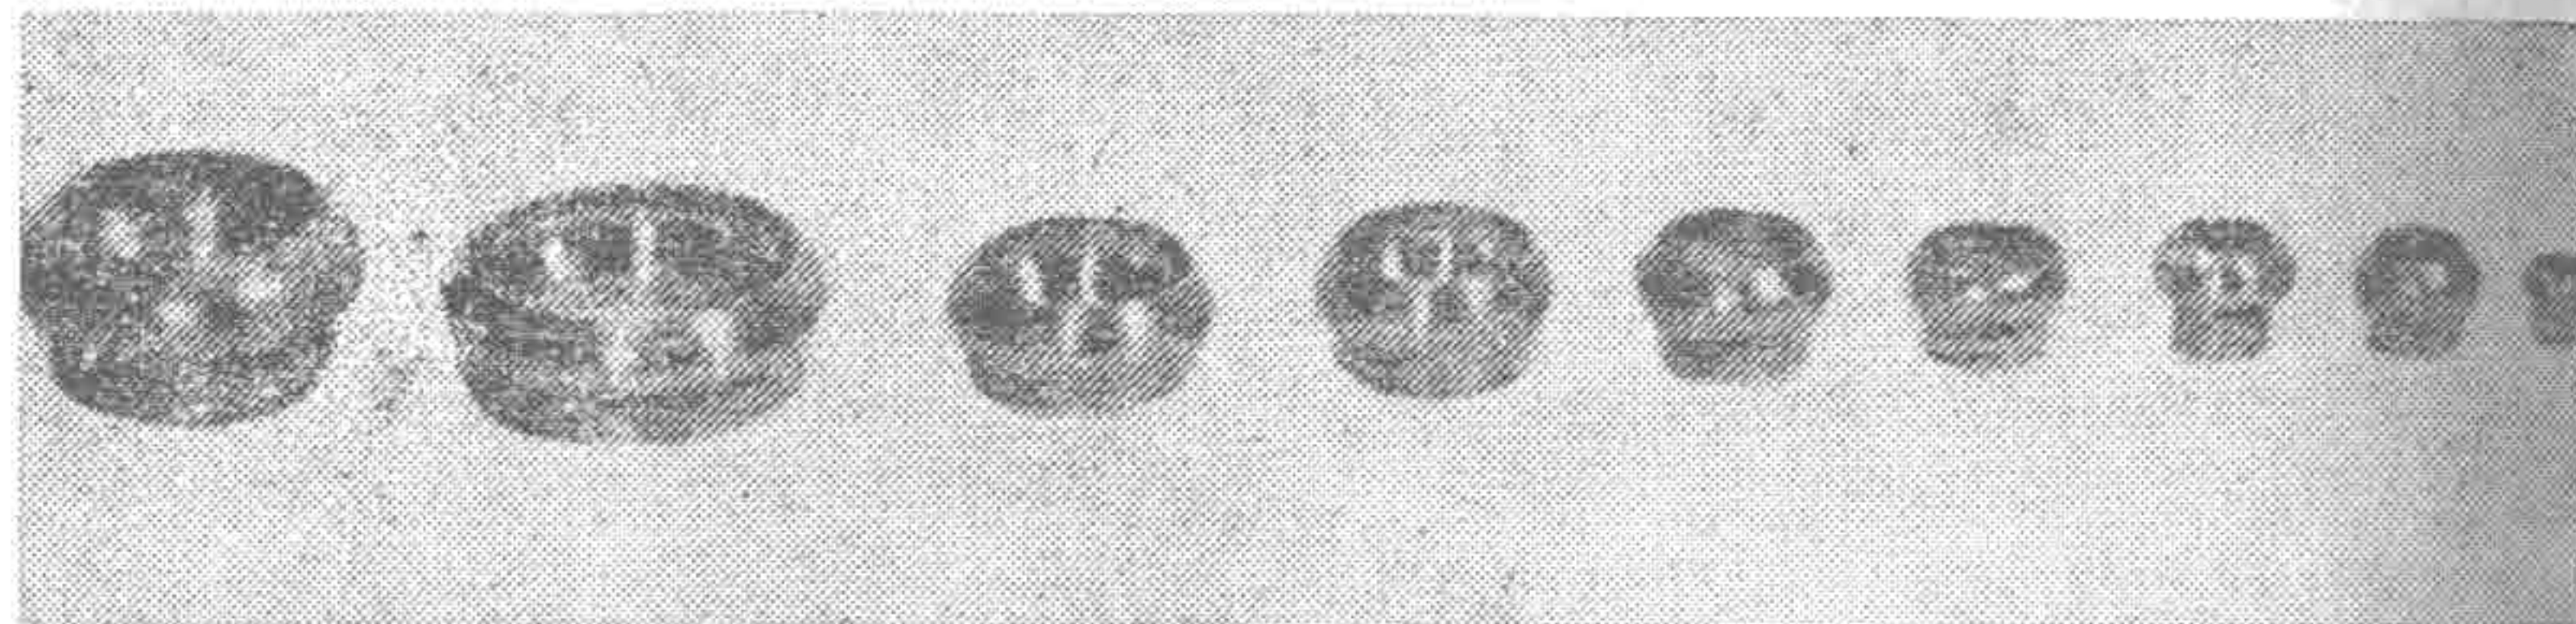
Детали, изготовленные на ЭГ прессах без резиновых уплотнений.
